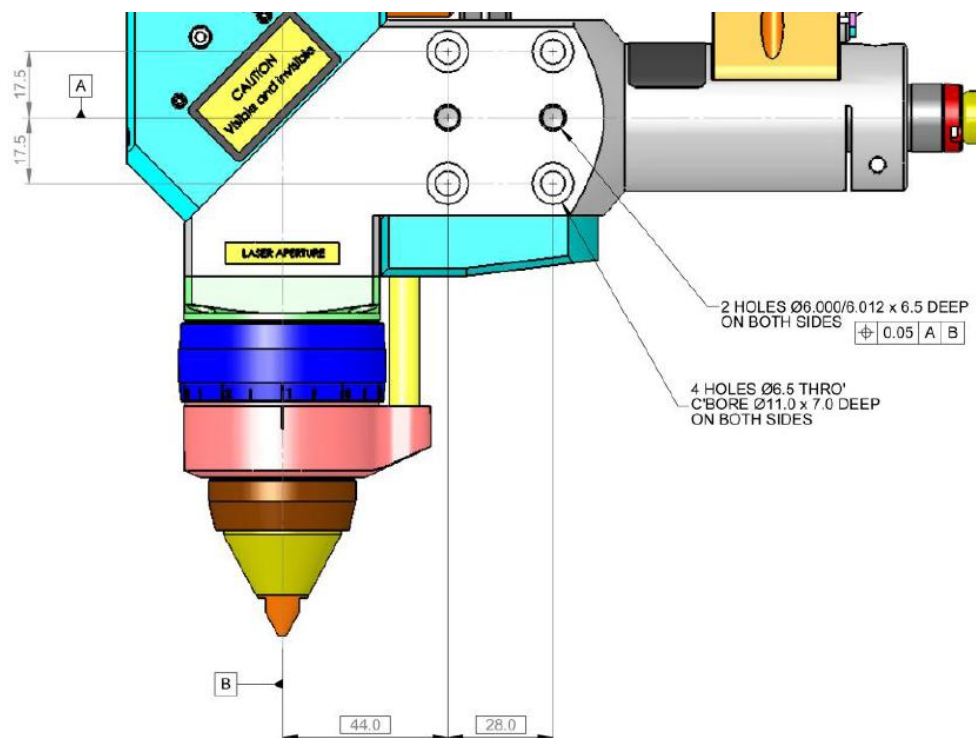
Uvažovaný prototyp CNC stroje [32]
